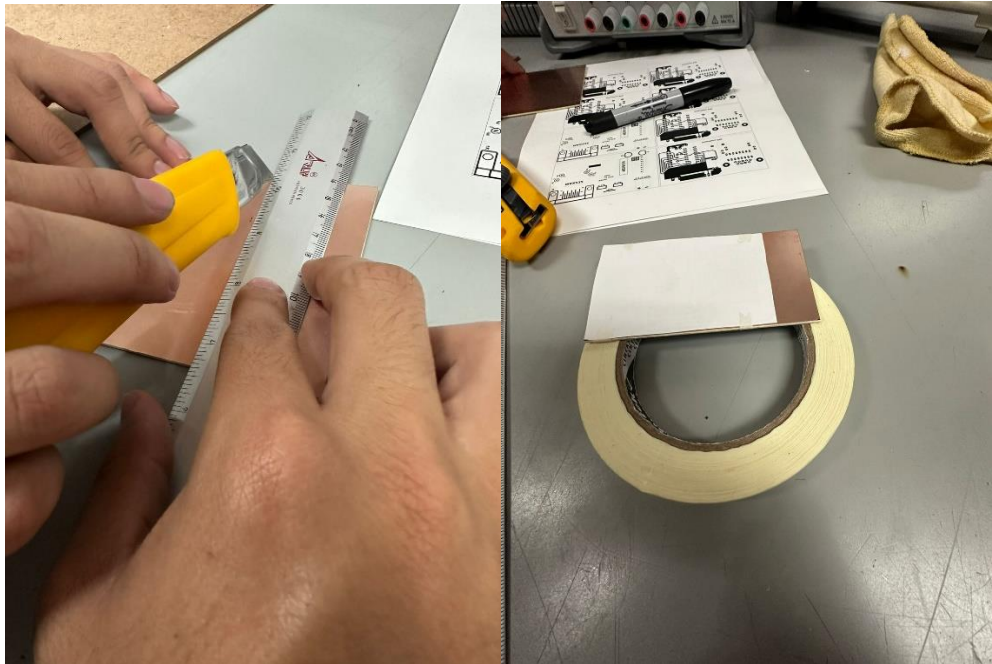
Se coloca la placa fenólica y el papel impreso.
